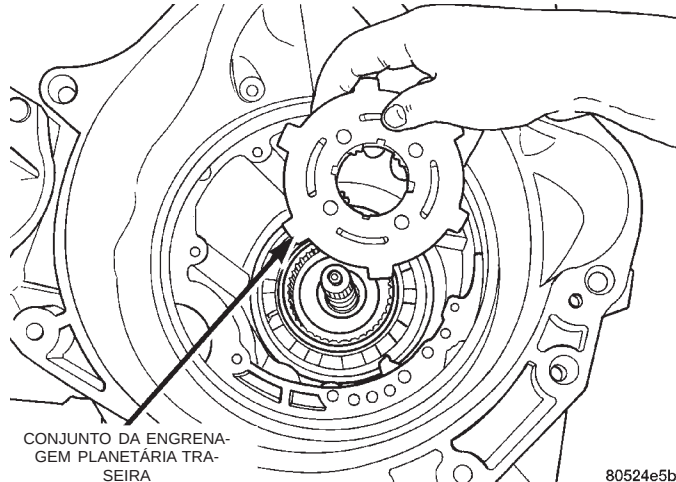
Conjunto da Engrenagem Planetária Traseira
